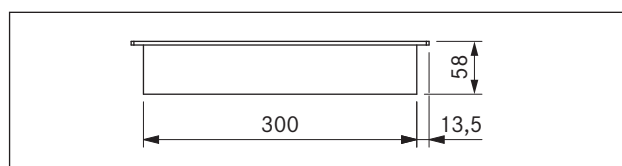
CKI apparatets dimensjoner sett forfra
